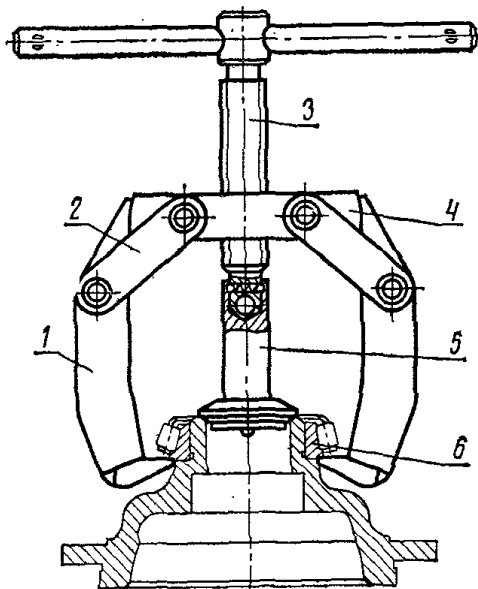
Гвинтовий знімач з лапчастими захватами: 1- захват; 2 - тяга; 3 - силовий гвинт; 4 - корпус; 5 - наставка; 6 - деталь
